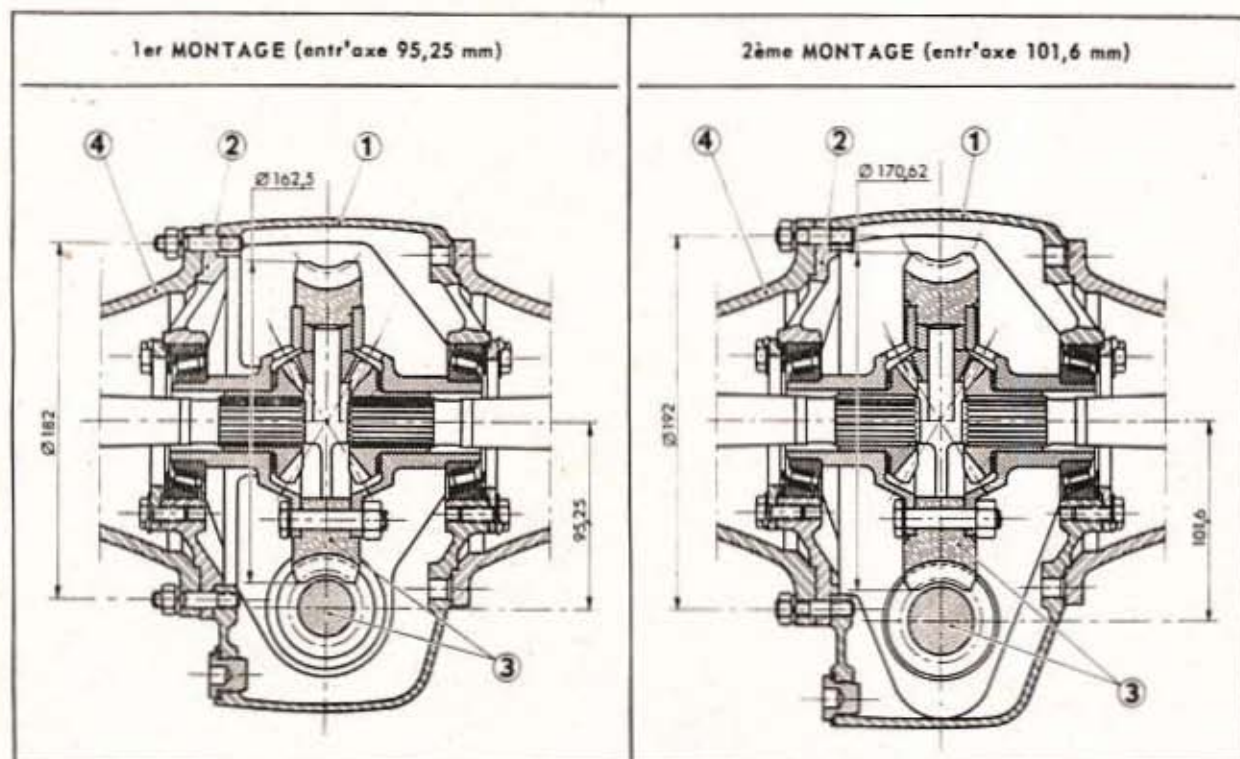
Vues en coupes des ponts à entr'axe de 95,25 et de 101,6 mm
